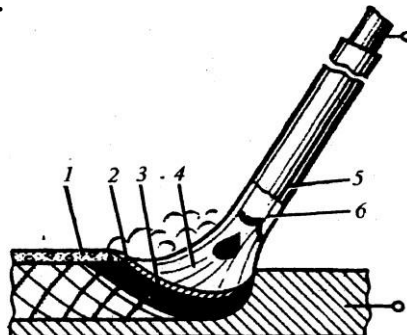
Схема дугового електричного зварювання металевим електродом:
